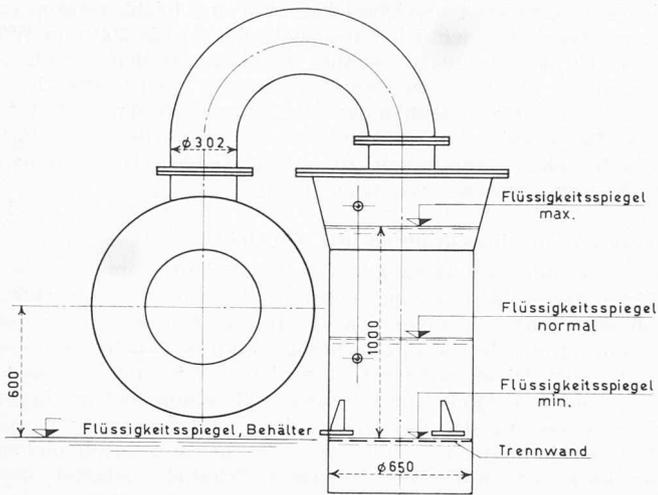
Druckausgleichsgefäß, Vertikalschnitt und Grundriss, 1:35
